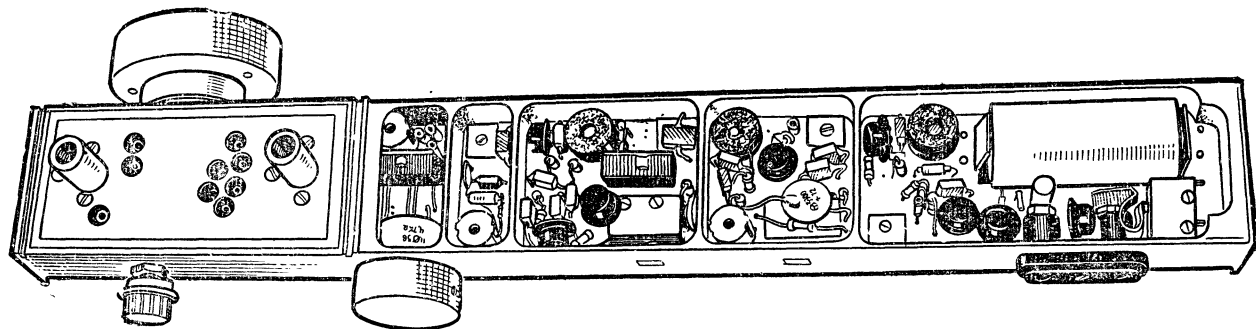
Внешний вид приемника со стороны расположения деталей (верхняя крышка снята).
